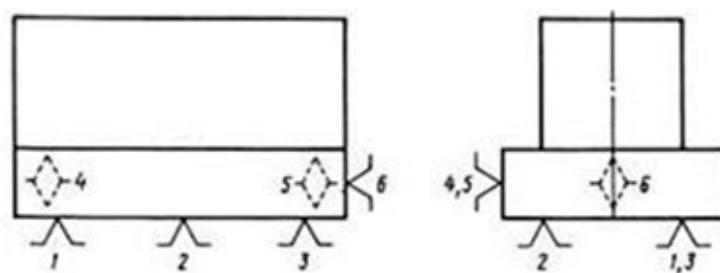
Базирование призматической заготовки в "координатный угол".
